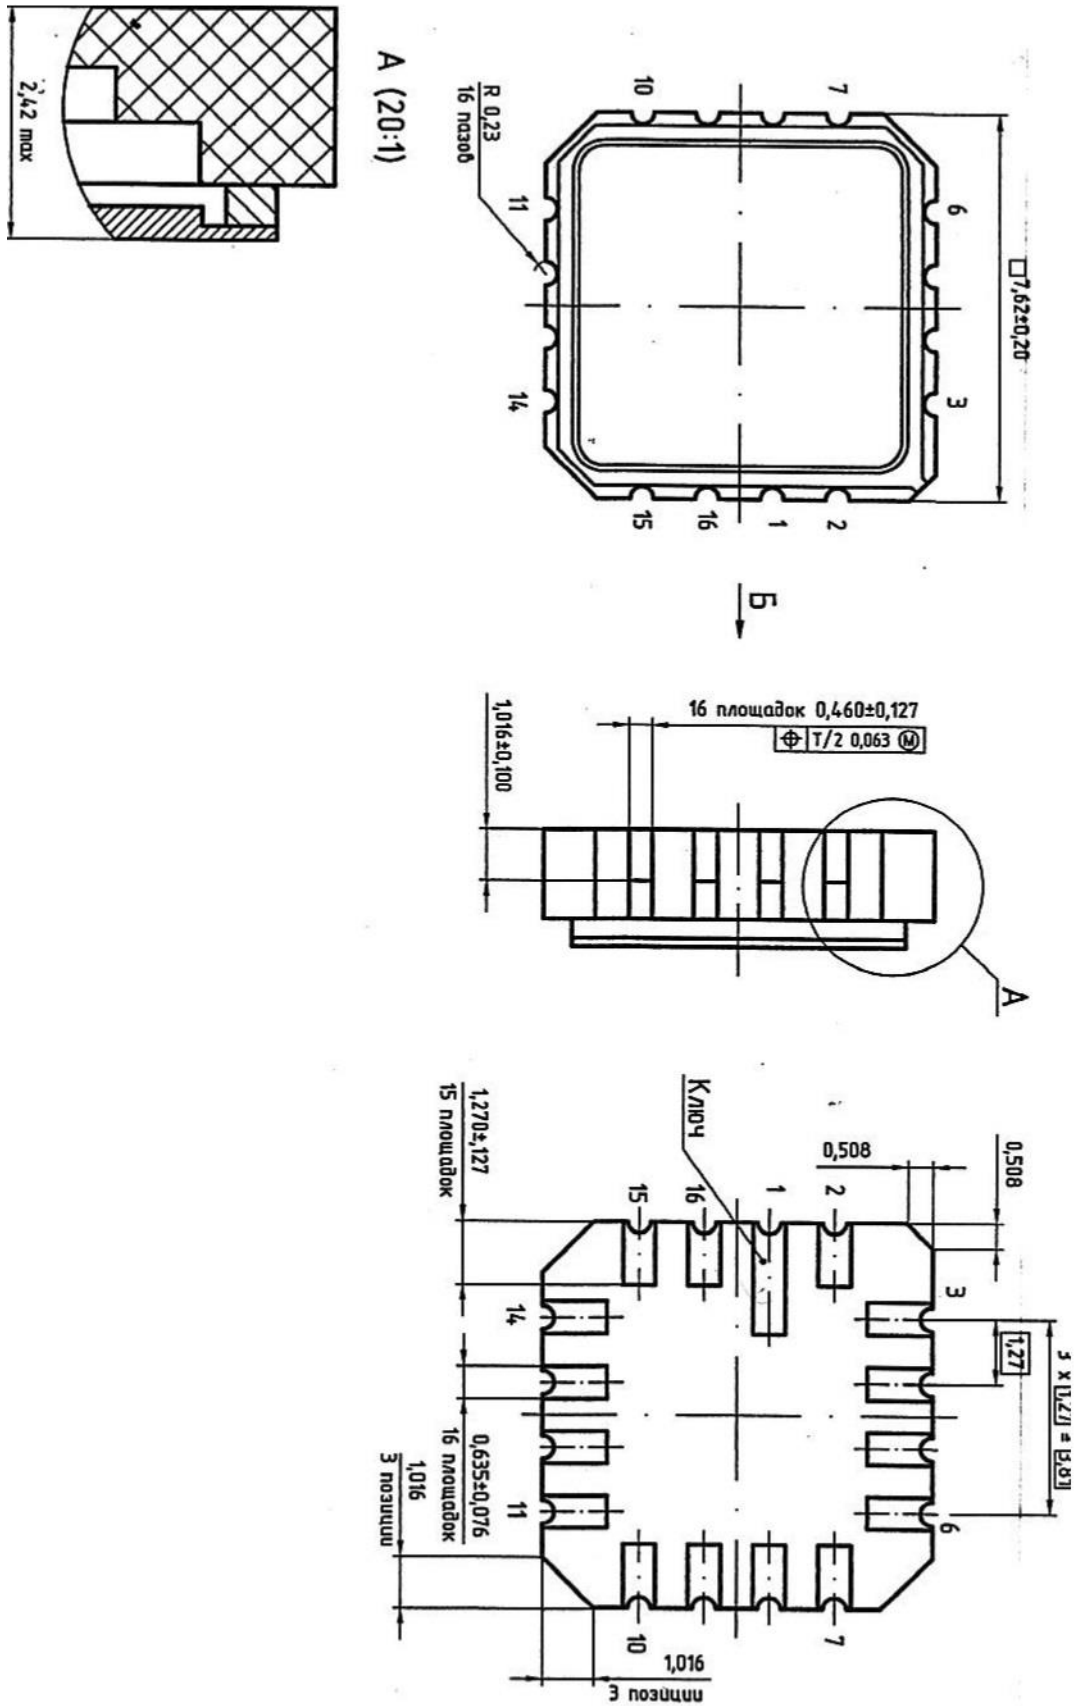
Габаритный чертеж корпуса 5119.16-А
